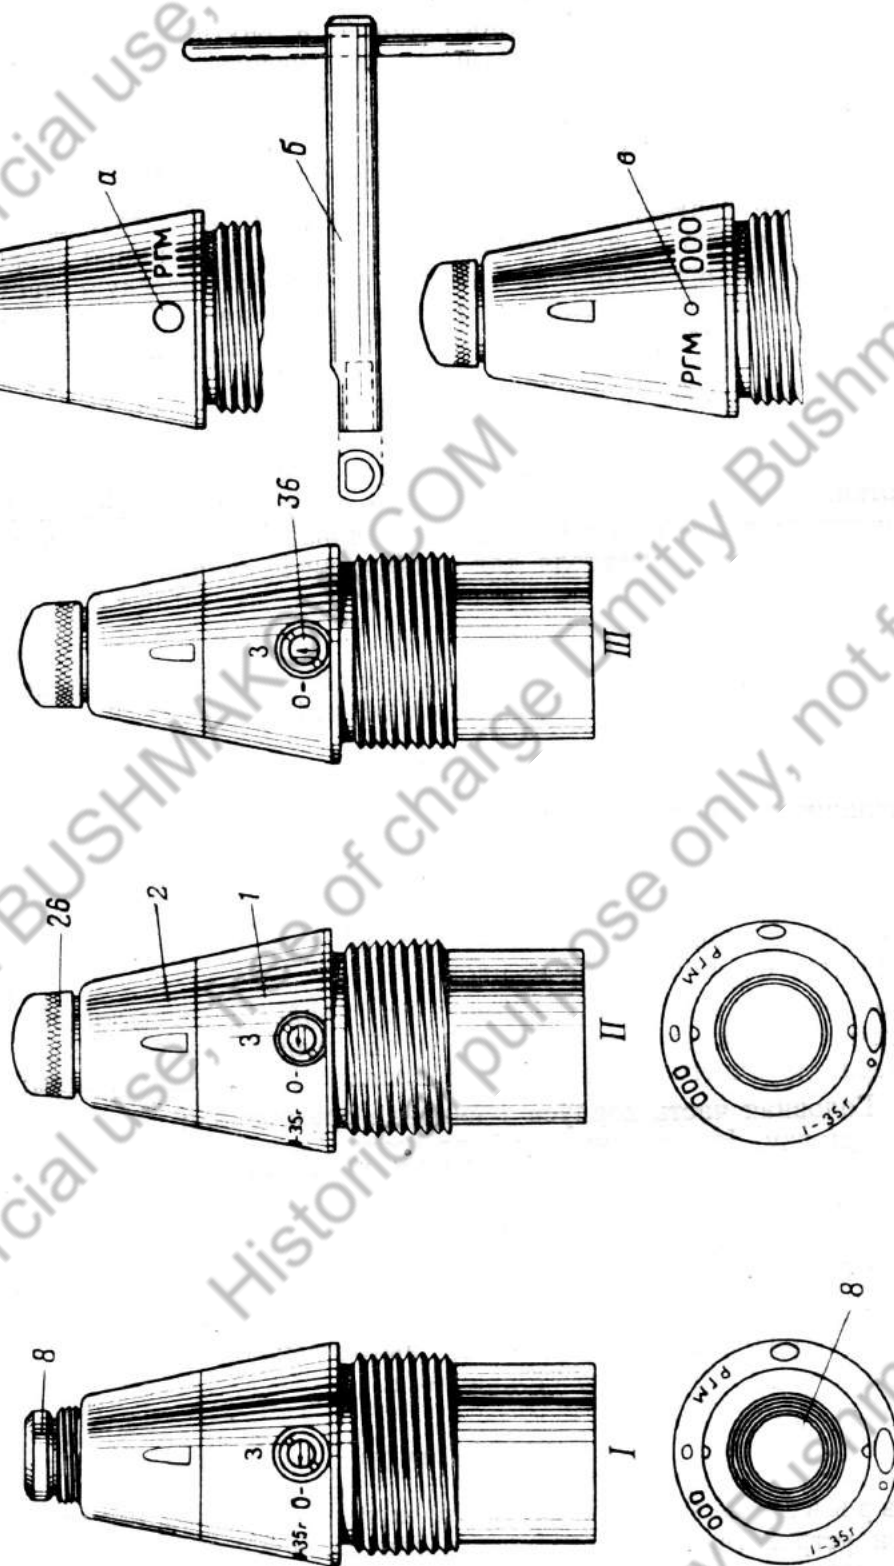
Общий вид взрывателя РГМ при различных его установках:
